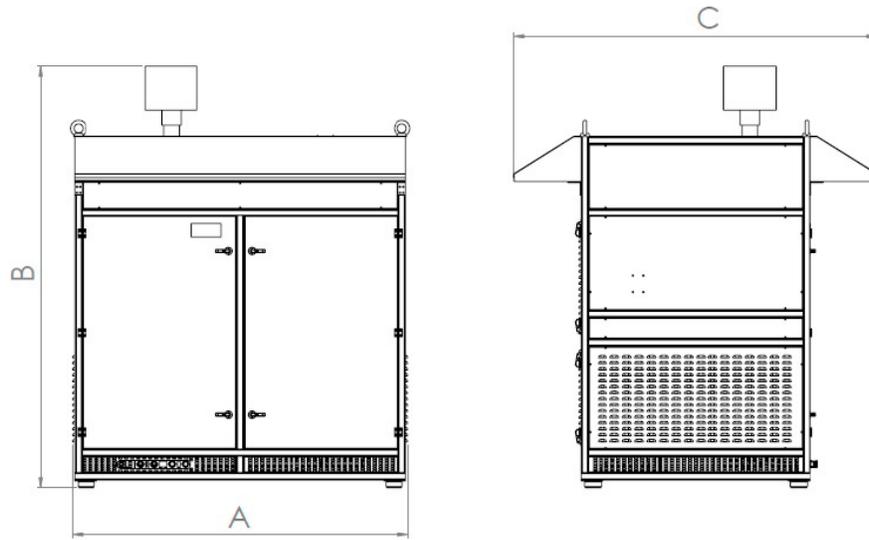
Dimensiones de calentamiento/compresor de aire/Tablero de control.
